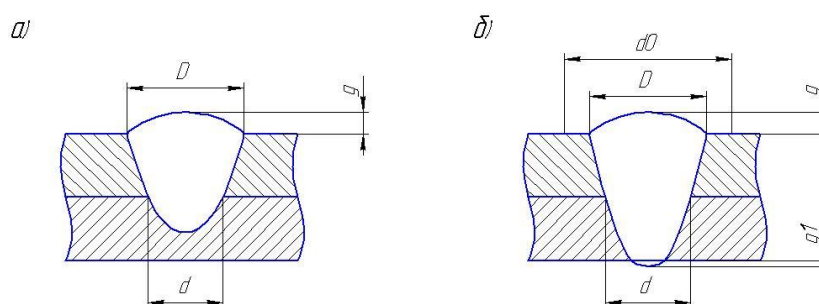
Сварка точками с частичным проплавлением (а) и полным проплавлением (б)
